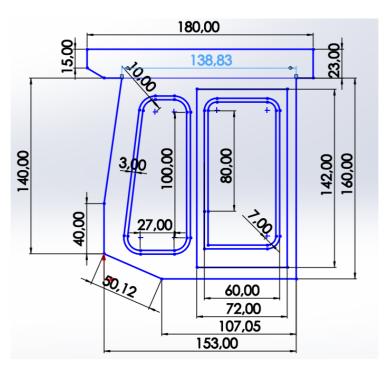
Vista Frontal del Diseño de la Cabina del Tractor CAMECO 505
